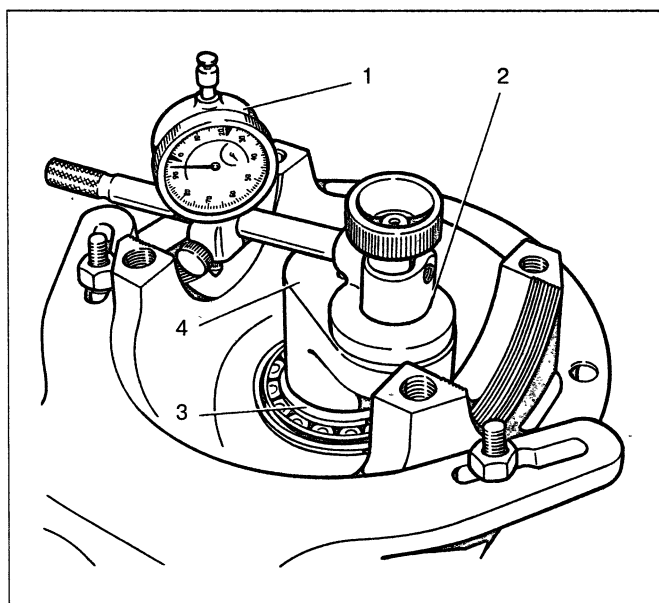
Определение толщины регулировочного кольца ведущей шестерни: 1 – индикатор; 2 – приспособление А.95690; 3 – задний подшипник ведущей шестерни; 4 – оправка А.70184
